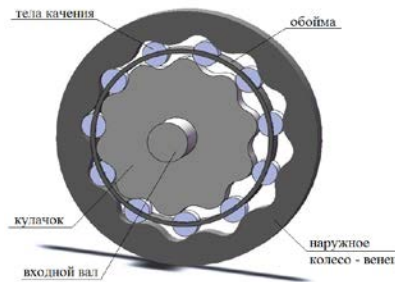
Схема зацепления передачи с промежуточными телами качения и свободной обоймой
